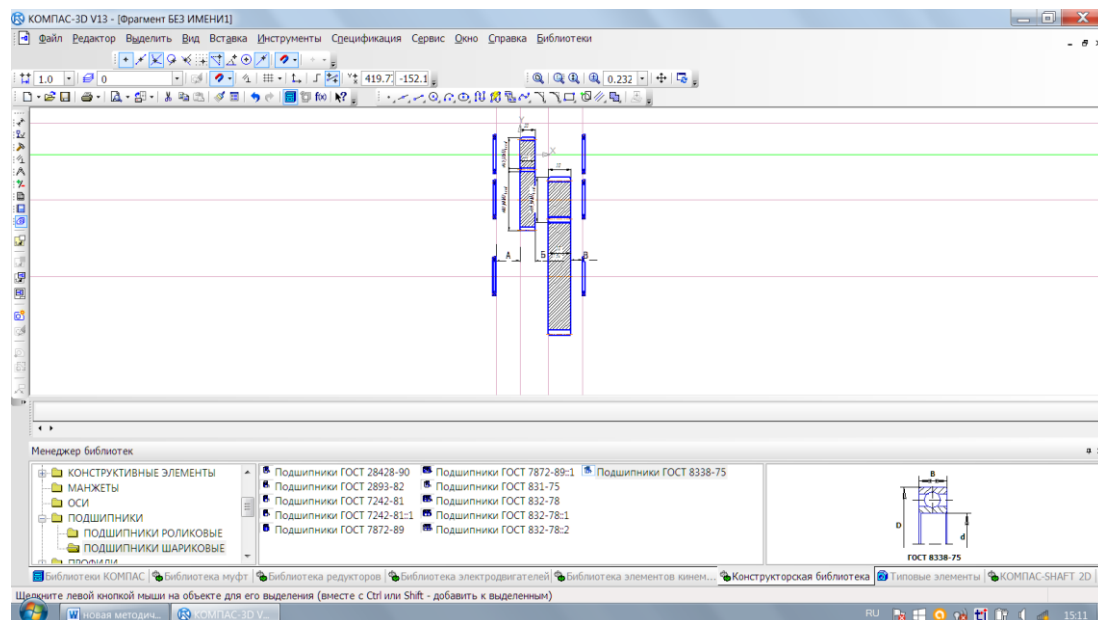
Применение библиотеки подшипников к эскизной компоновке редуктора
